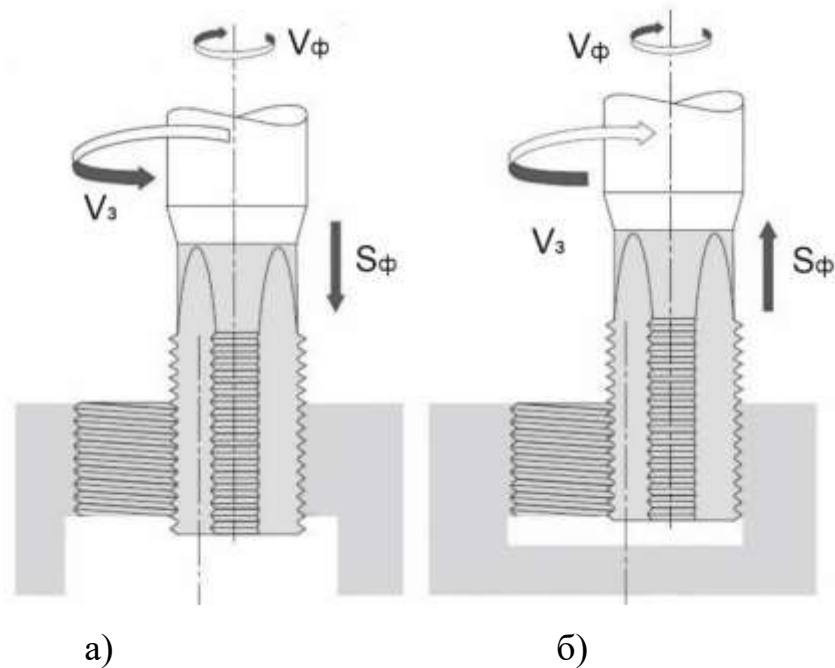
Схема фрезерування правого внутрішнього різьблення:
